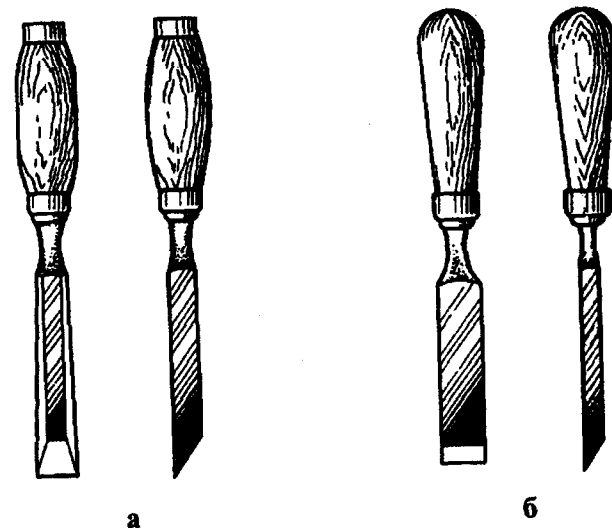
Инструменты для выдалбливания проушин: а — долото; б — стамеска;
